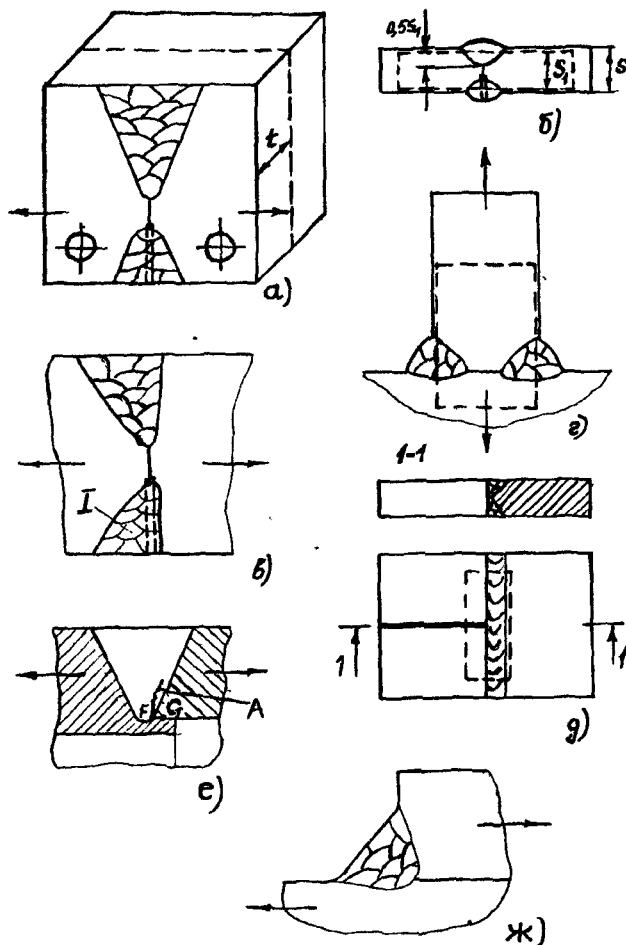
Сварные образцы с технологическими дефектами
